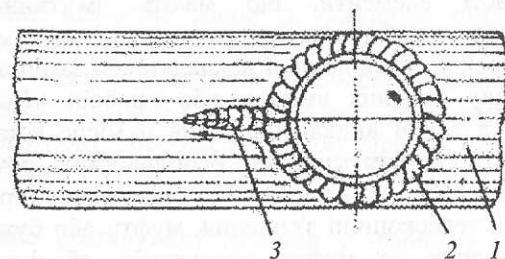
Зварювання трубчастих з'єднань із «вусом»:
